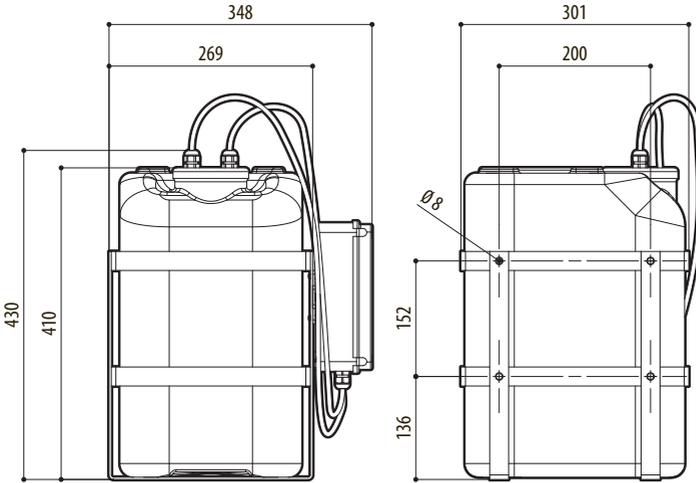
Réservoir 23l, hauteur de remontée de 5m.
